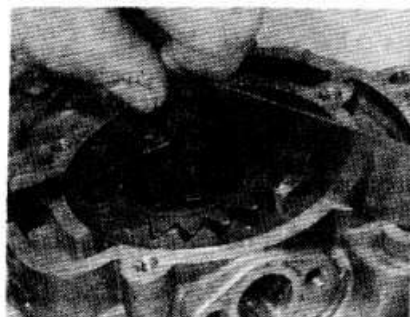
и между торцевой поверхностью зубьев и корпуса
